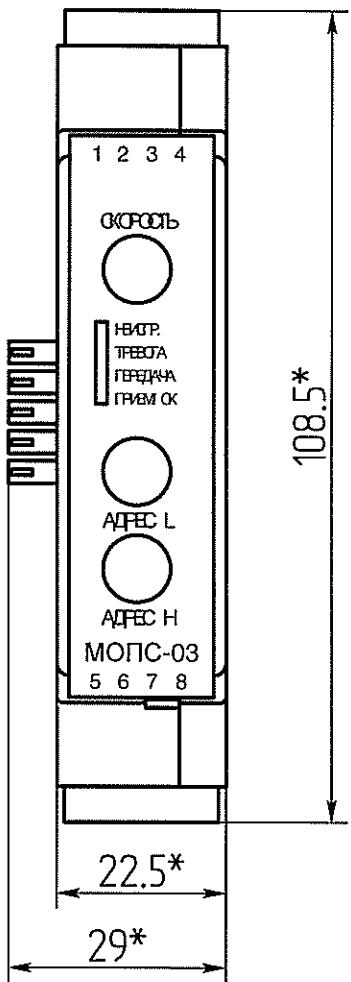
Внешний вид модуля МОПС-03 с шинным соединителем
